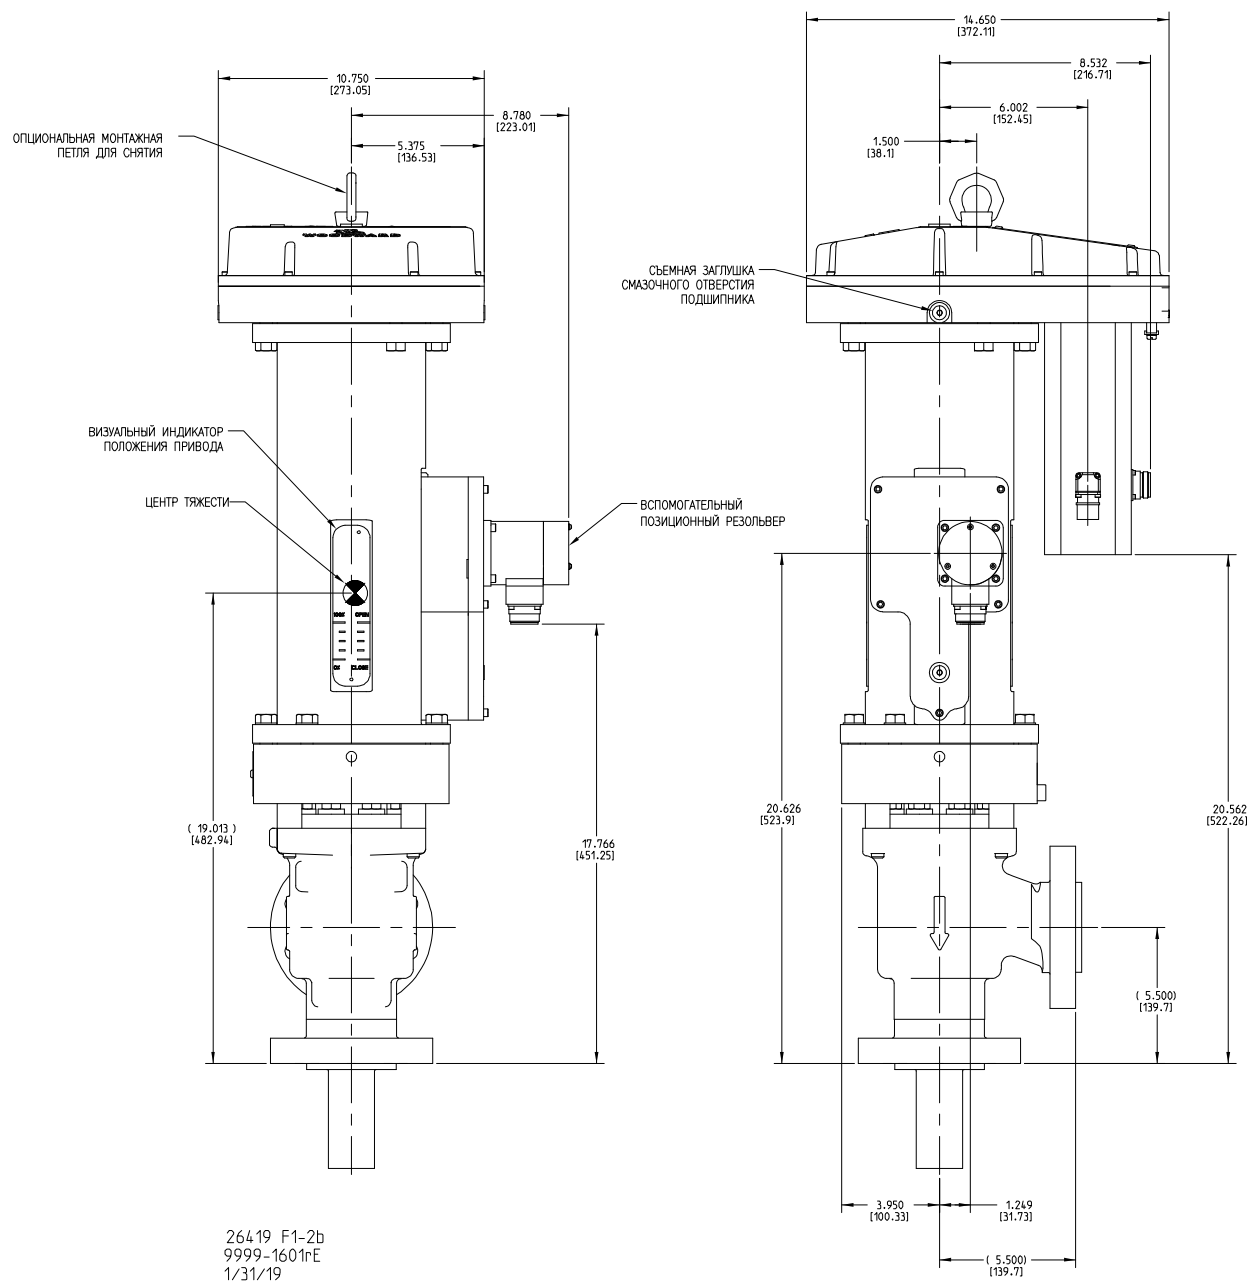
Габаритный чертеж (2-дюймовый клапан LESV класса 600)
